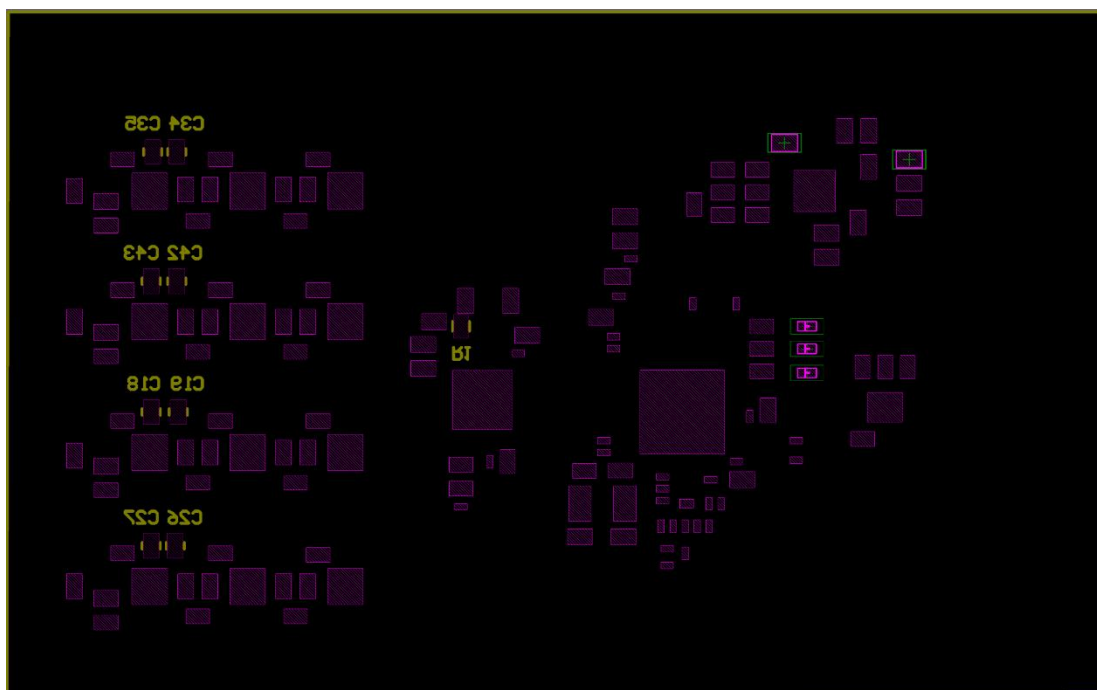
Bottom overlay de la placa de circuit impreso (PCB). (Fuente propia).
